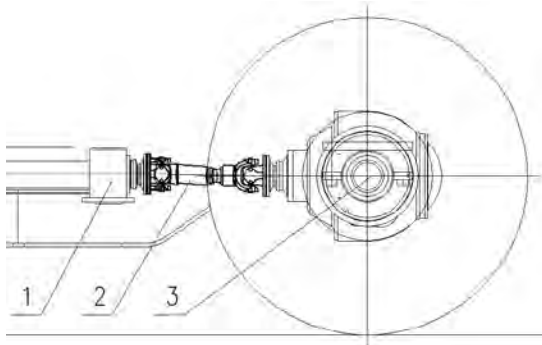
Схема установки двухшарнирной карданной передачи на машине: 1 – опора; 2 – карданный вал; 3 – задний мост с колесами
